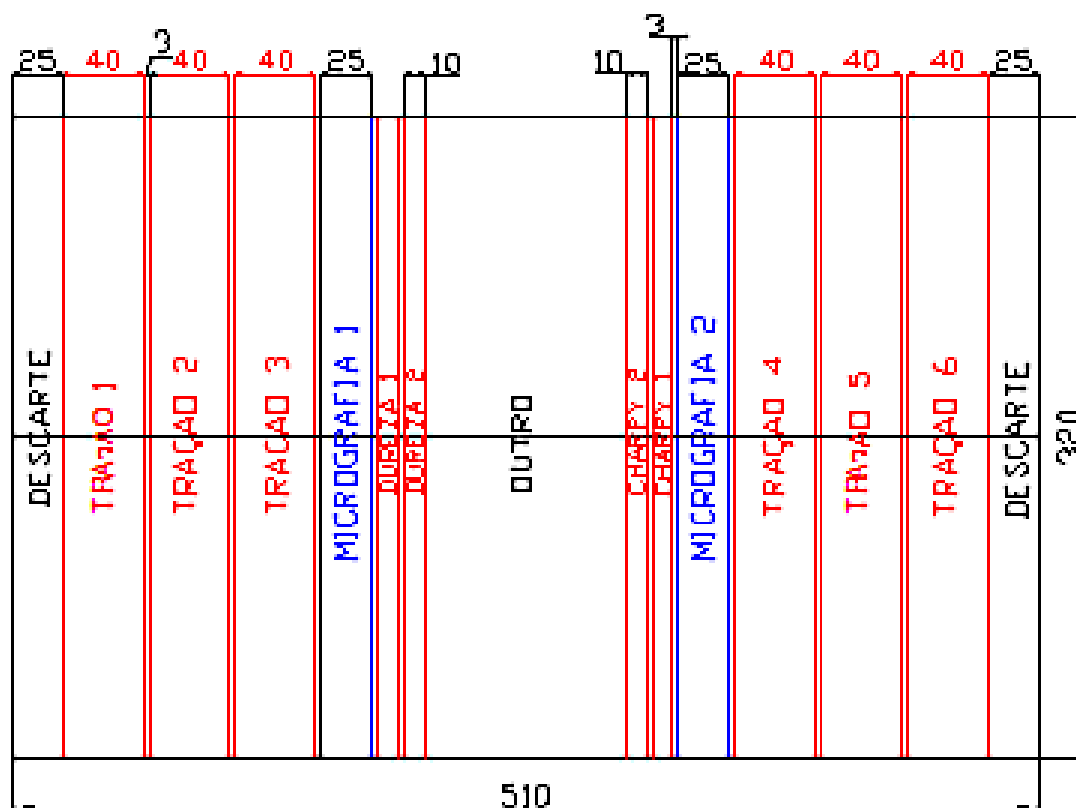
Dimensões do corpo de prova de soldagem.
